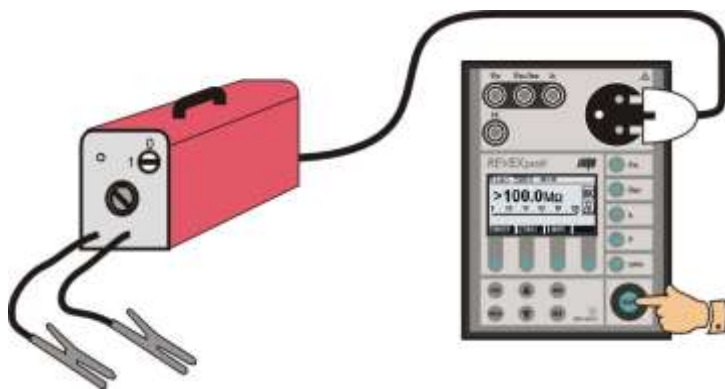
Měření odporu ochranného obvodu trojfázové svářečky
